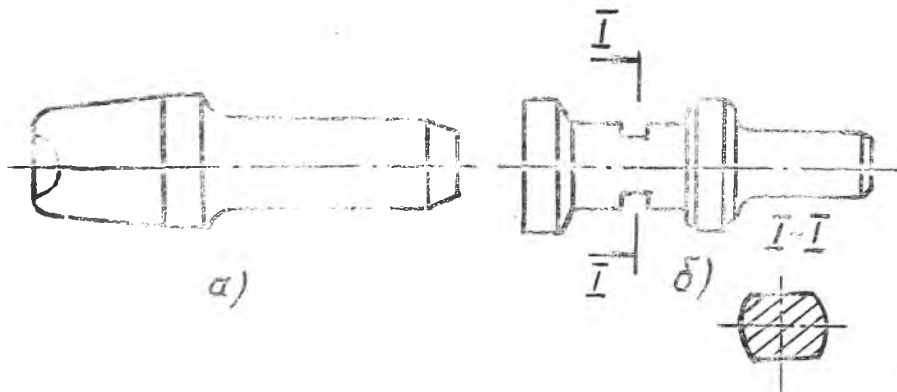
Облицовки для напайки пневматическими молотками: а) пневматический молоток без выбросового устройства; б) пневматический молоток с выбросовым устройством.
